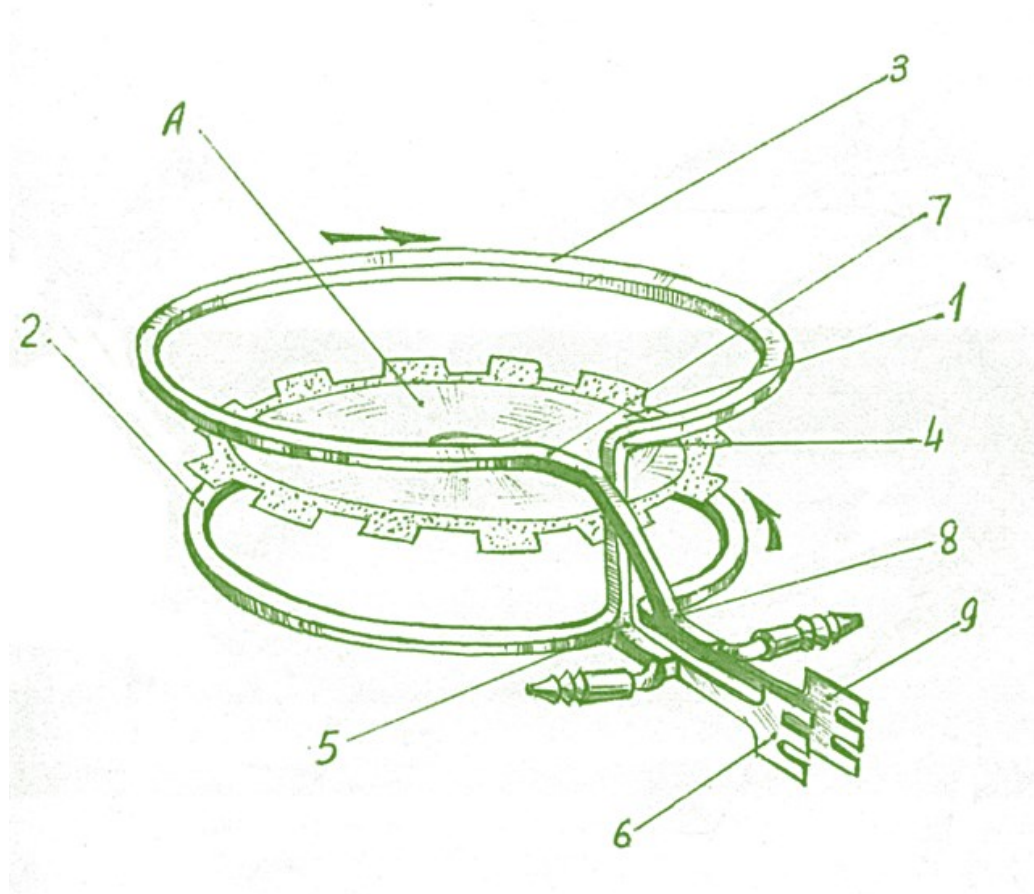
Двовитковий кільцевий індуктор для наплавлення тонких дисків зубчатої форми з прямокутним однаковим поперечним перерізом і різними діаметрами витків [51, 58,59]: 1 - диск; 2 - нижній виток; 3 - верхній виток; 4 - місце з'єднання верхнього витка з нижнім витком; 5 - місце з'єднання нижнього витка з штуцером для подачі води; 6 - ліва клемма; 7 - місце з'єднання другого кінця верхнього витка з нижнім витком; 8 - місце з'єднання нижнього витка з штуцером для відводу води; 9 - права клемма індуктора
